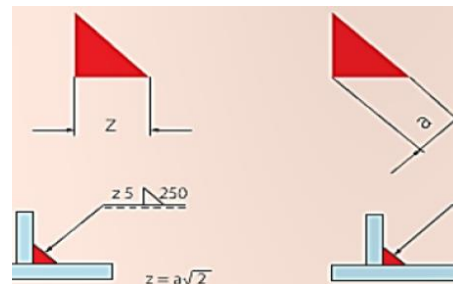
Representação Esquemática Cateto de soldadura (Silva F. J., 2016)
